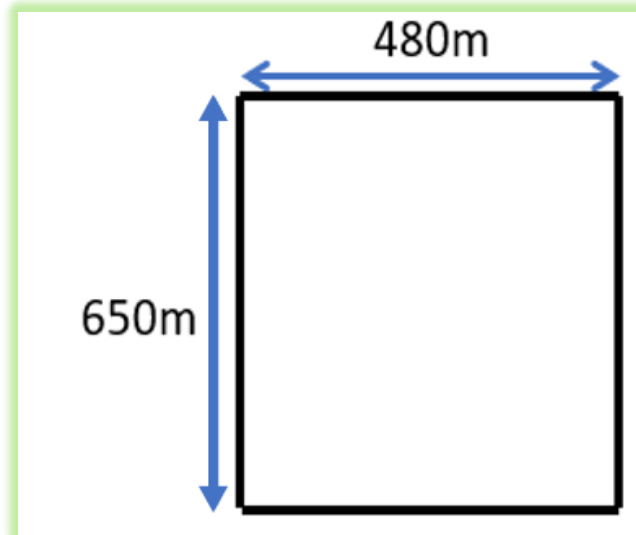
Dimensiones del chasis para ensamblar la caja de dirección
